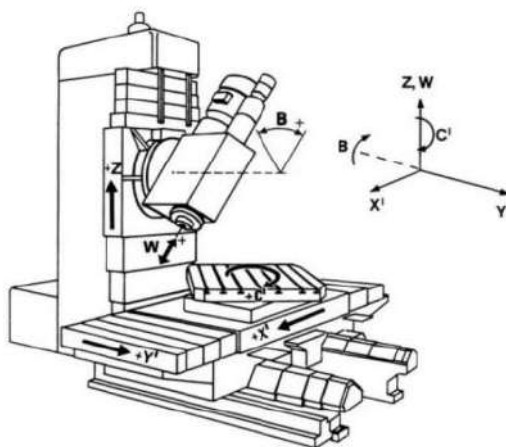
Фрезерний верстат з можливістю кутової обробки
